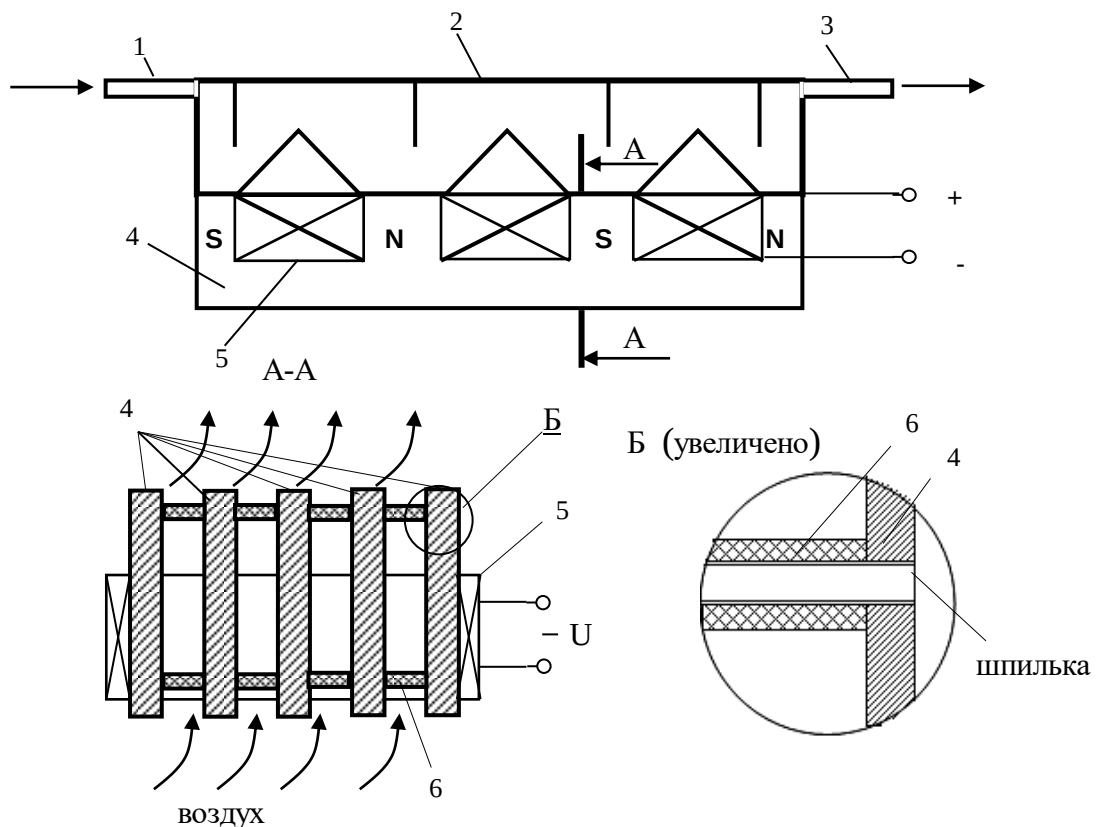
Схема отстойника с *III* - образной формой сердечника электромагнита: 1- входной патрубок; 2 - рабочая камера; 3 - выходной патрубок; 4 - магнитопровод; 5 – обмотка; 6 - немагнитные втулки.
